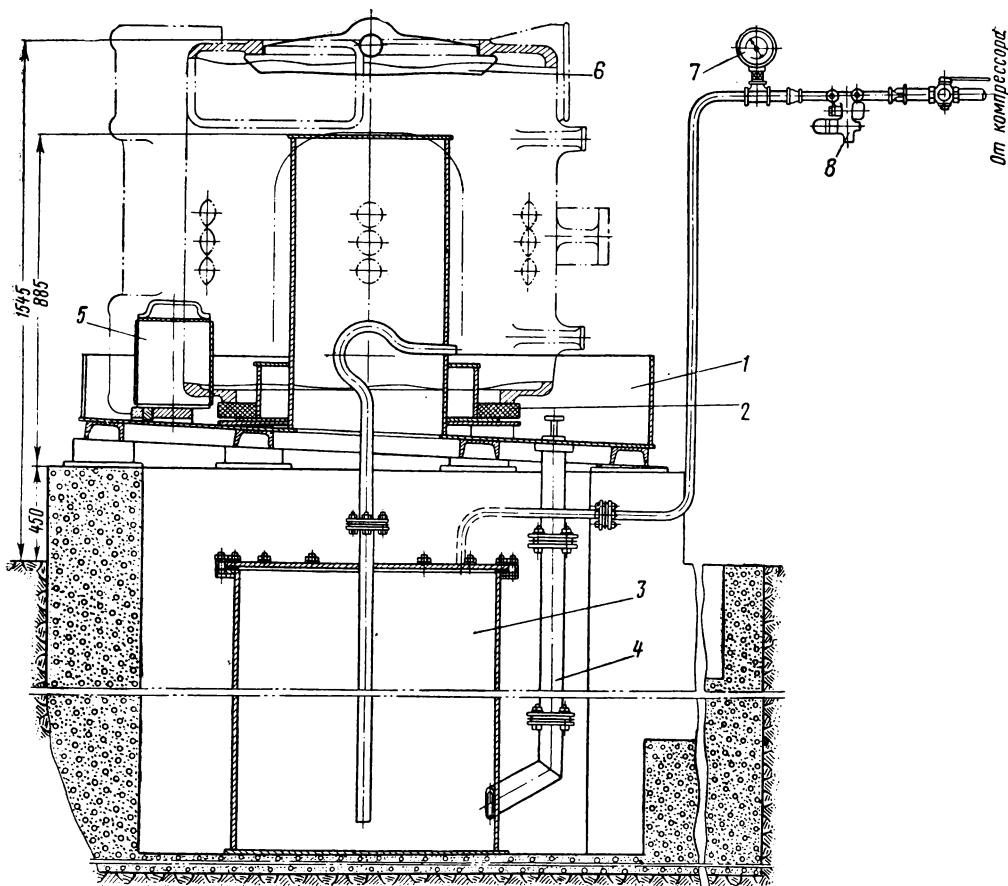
Установка для пропитки катушек тяговых двигателей без снятия их с остова: 1 — поддон; 2 — уплотняющее кольцо; 3 — бак для лака; 4 — труба спускная; 5 — фиксатор; 6 — захват; 7 — манометр; 8 — золотниковый питательный клапан
